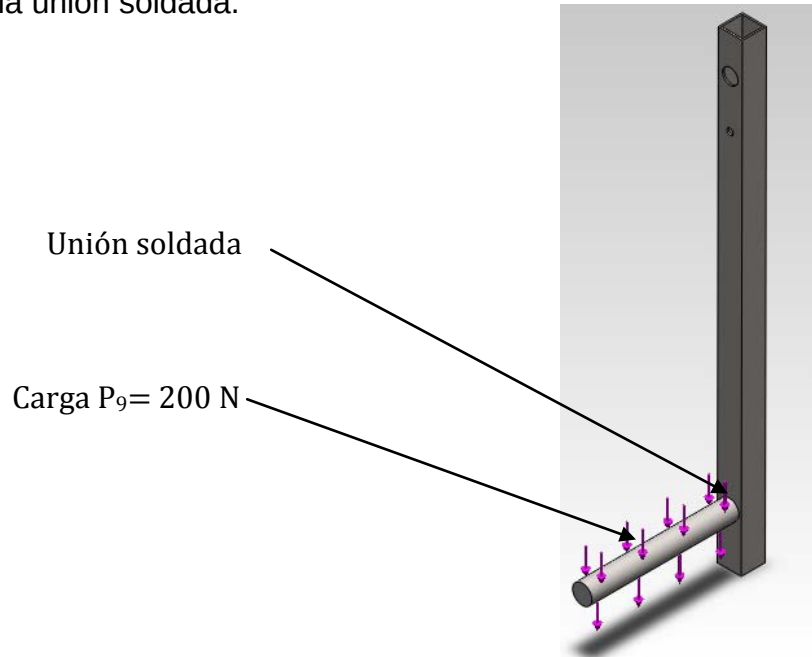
Cargas aplicadas en la soldadura en la pieza N°5
